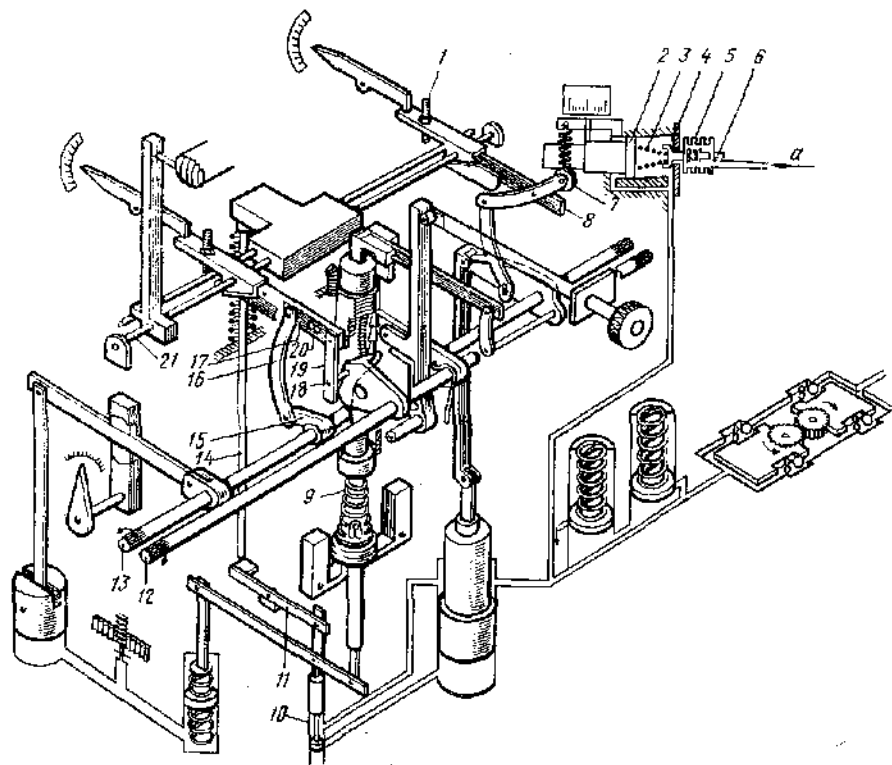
Кинематическая схема регулятора «Вудвард» (модификация UG-40TL): 1-регулирующий винт; 2-поршень; 3-установочная пружина; 4-клапан; 5-сильфон; 6-установочный винт; 7-ролик; 8, IV, 77-рычаг; 9-пружина задания; 10-золотник; 12, 13-вал; 14-выключающий шток; 15-длинный штифт; 16-тяги; 17-штифты кривошипа; 19-планка; 20-штифты рычага; 21-ось
